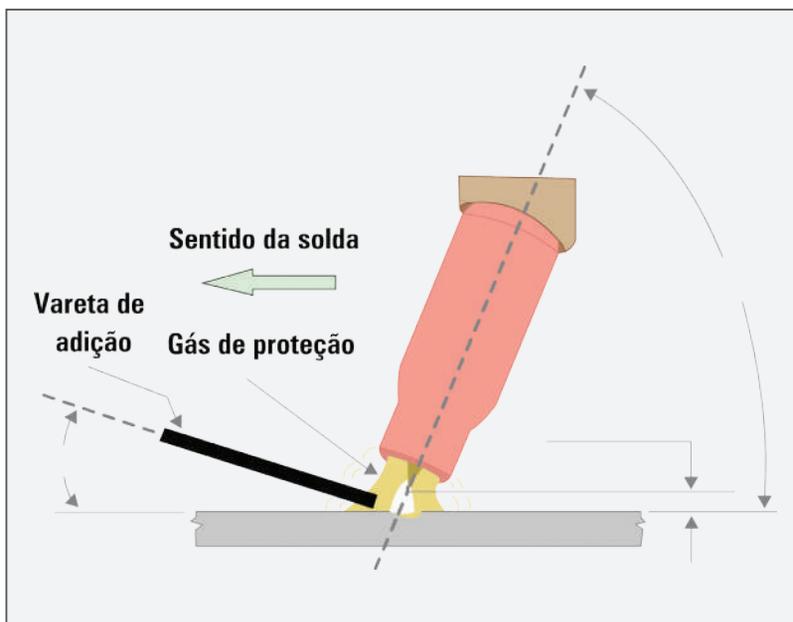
Posição da tocha e vareta de adição para a soldagem plana
